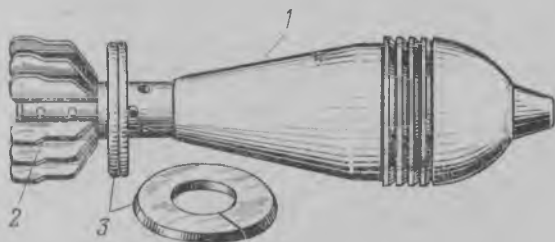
82-мм мина с дополнительными зарядами: 1 — корпус мины; 2 — стабилизатор; 3 — дополнительные заряды
